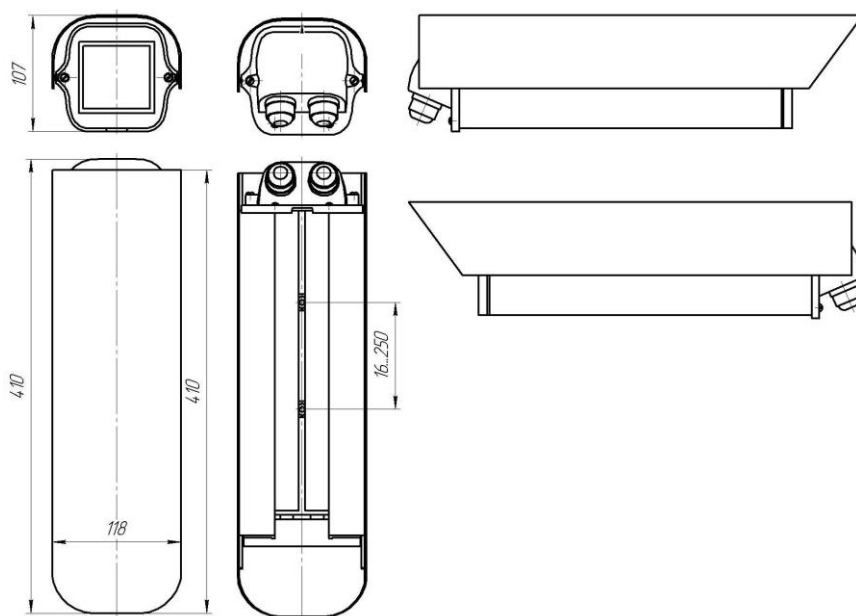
Габаритные размеры видеокамеры СВК-856
